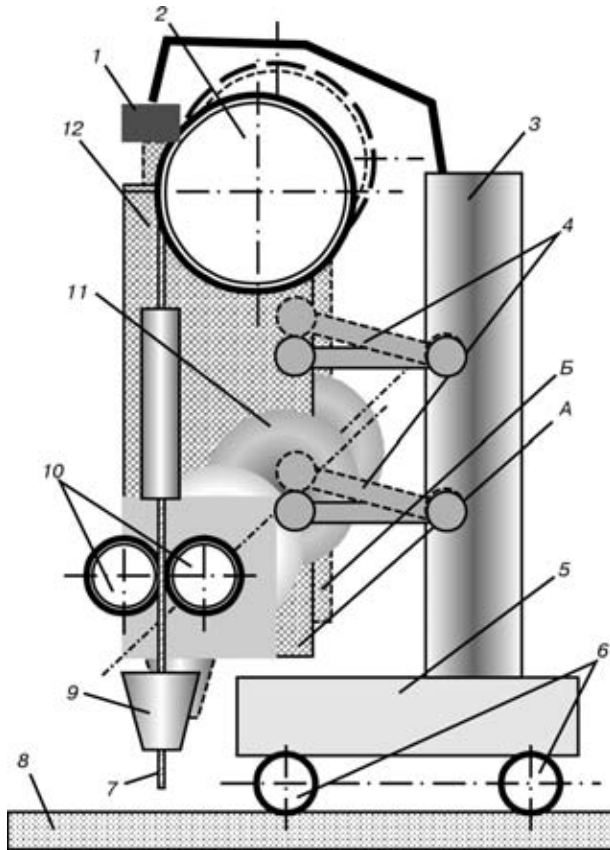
Фрагмент системы возбуждения дуги под флюсом: 1 — датчик; 2 — кассета с электродной проволокой; 3 — стойка; 4 — подвеска корпуса; 5 — тележка; 6 — привод перемещения автомата; 7 — электродная проволока; 8 — свариваемое изделие; 9 — токоподводящий наконечник; 10 — подающий и прижимной ролики; 11 — электродвигатель механизма подачи; 12 — корпус с механизмом подачи
